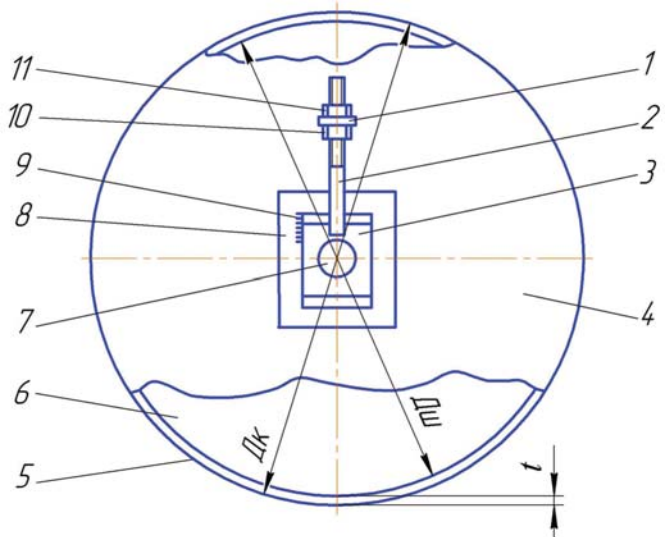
Механізм регулювання зазору між нижньою частиною шнека і кожухом: 1 – упор; 2 – регулювальний гвинт; 3 – корпус підшипника вала шнека; 4 – верхня торцева частина кожуха шнека; 5 – кожух шнека; 6 – шнек; 7 – цапфа вала шнека; 8 – напрямна корпусу підшипника; 9 – шкала; 10, 11 – регулювальні гайки
